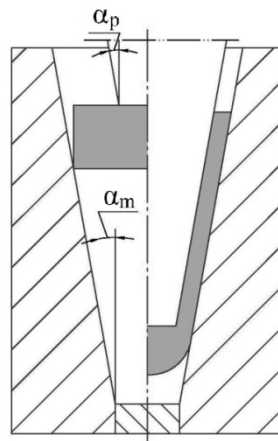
Схема процесса комбинированного выдавливания полый конической детали
